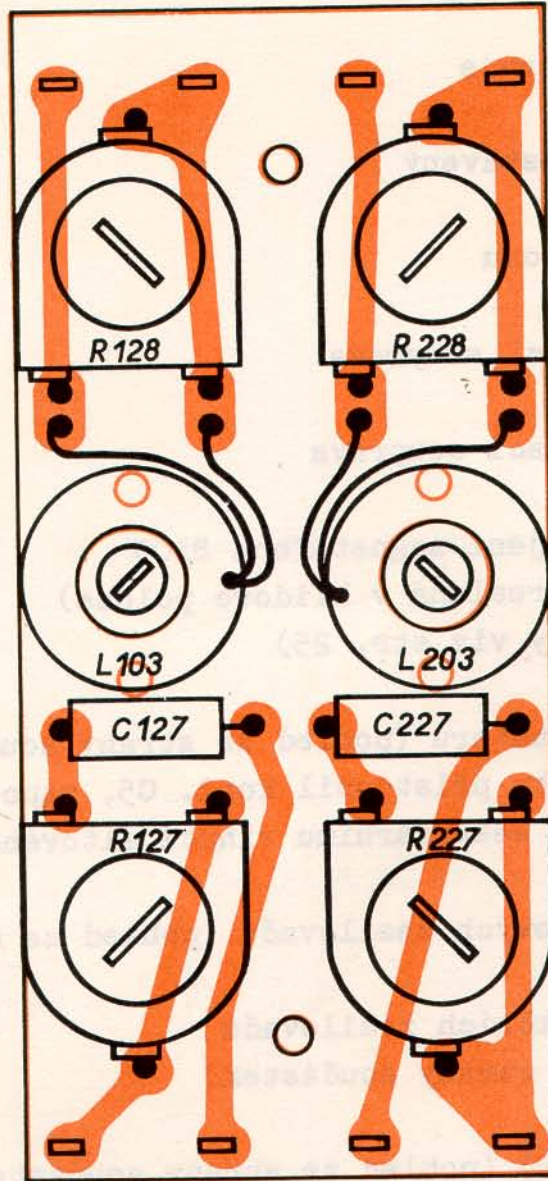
Deska eliminátoru (pohled ze strany součástek)
